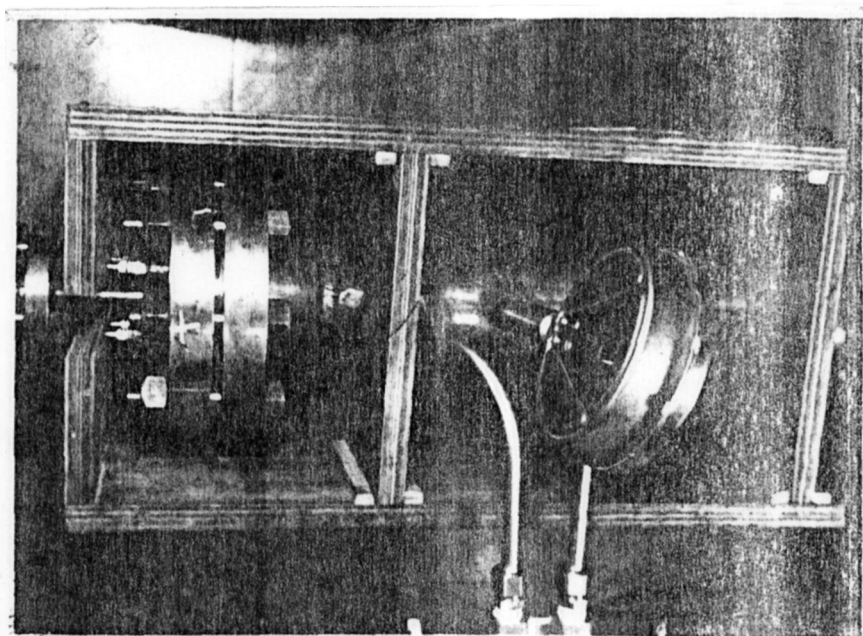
Flange do tipo "Welding Neck", anel intermediário e contra flange instalados no vaso de pressão.
